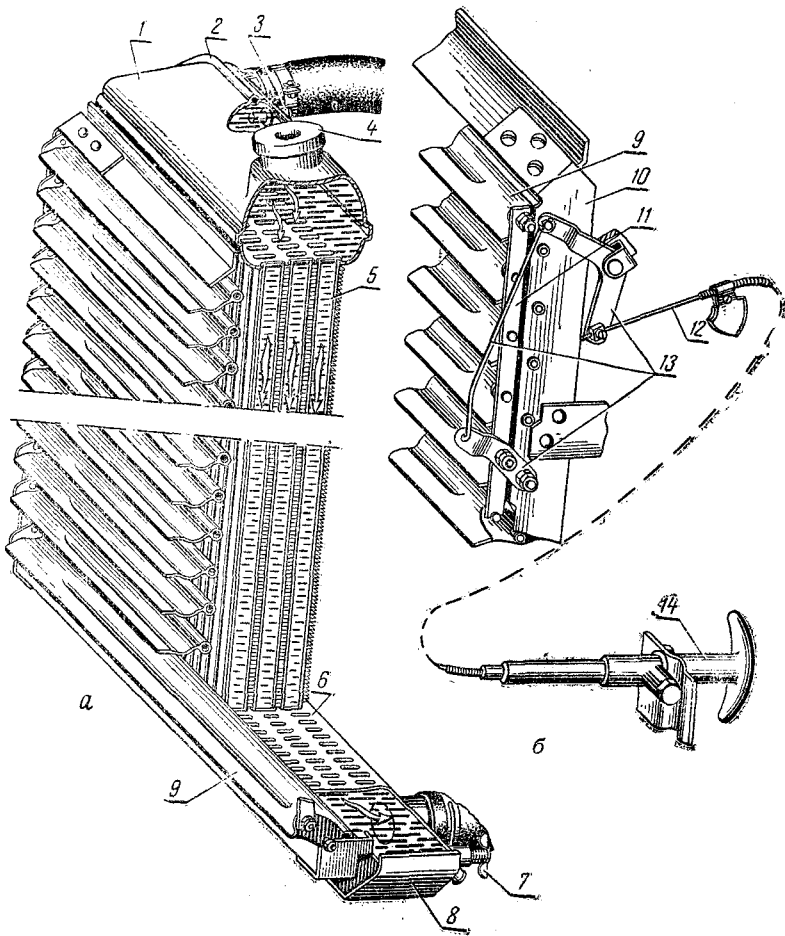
Устройство и управление жалюзи радиатора двигателя ГАЗ-53:
